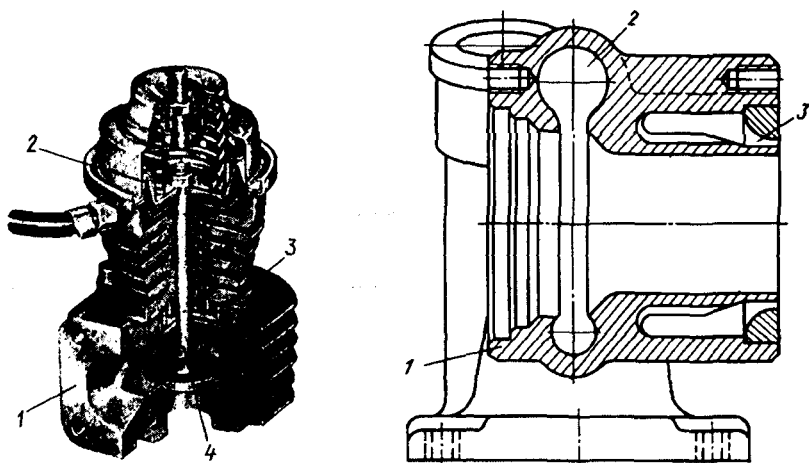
Встроенный регулирующий клапан тарельчатого типа фирмы ККК: 1 — корпус клапана; 2 — диафрагма; 3 — экран; 4 — тарельчатый клапан
